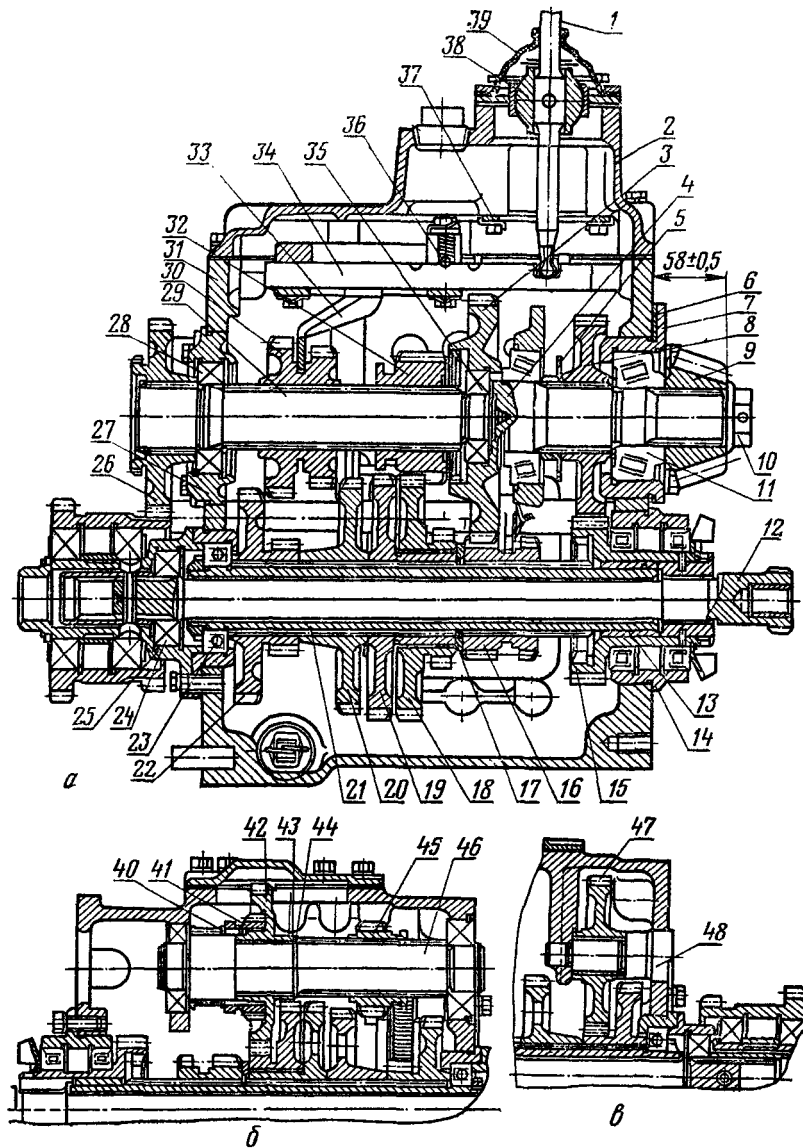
Коробка передач тракторов МТЗ-80 и МТЗ-82:
